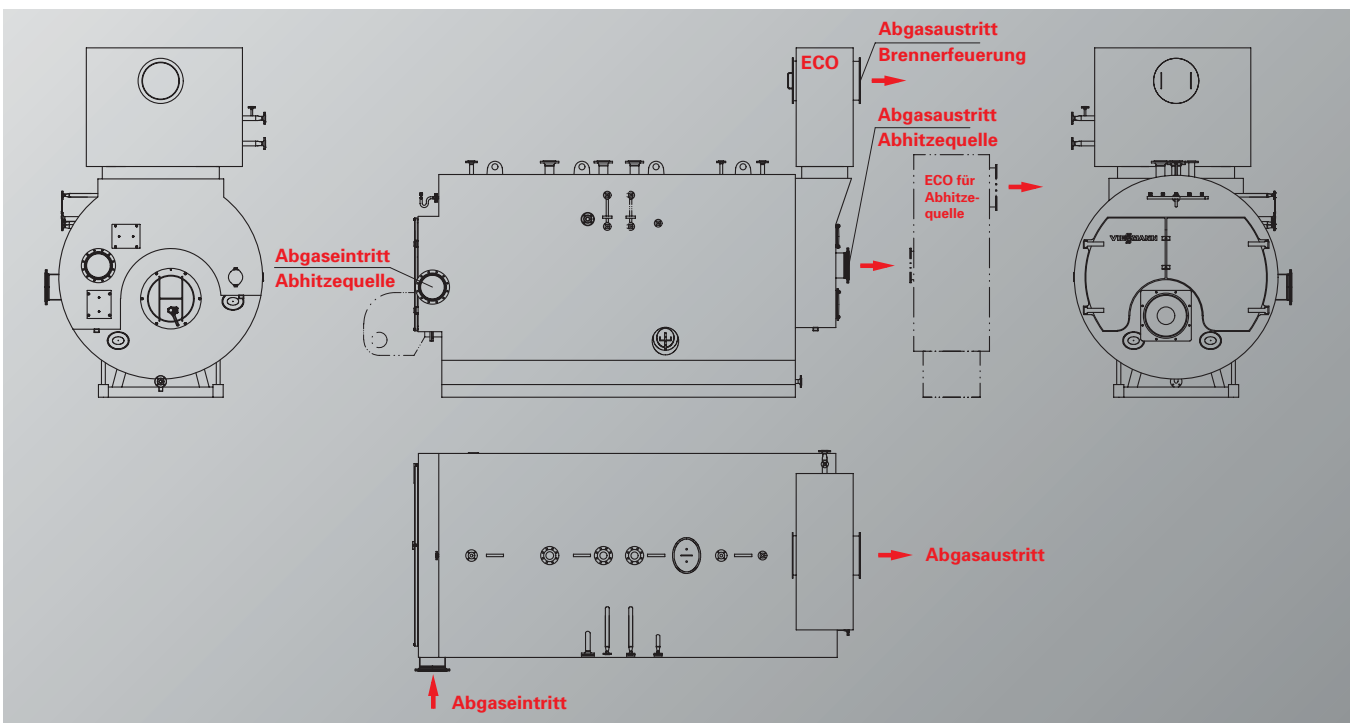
Großwasserraumkessel zur Dampferzeugung mit einem Abhitzezug (Alle weiteren Kesselanschlüsse entsprechen den konventionellen Dampf- bzw. Heißwassererzeugern).
